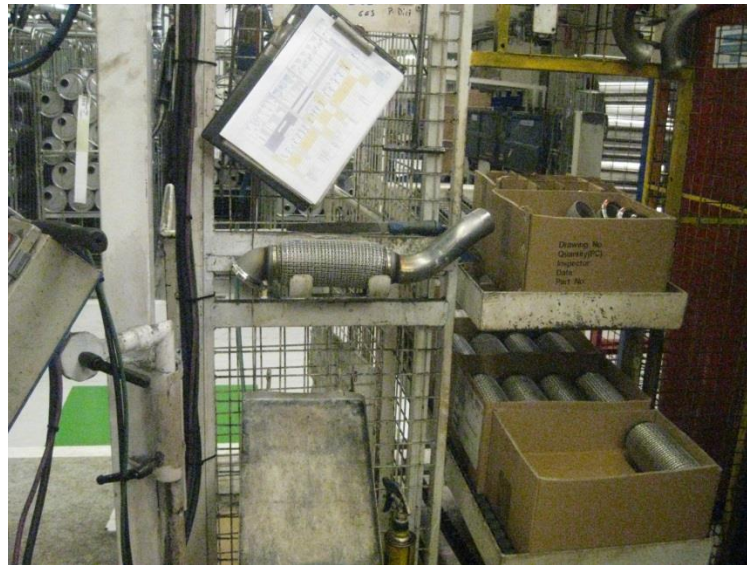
Soporte para subconjunto flexible (parte izquierda)
